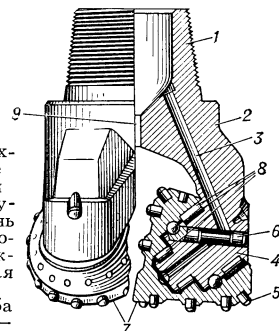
Трёхшарошечное долото для сплошного бурения в очень крепких породах: 1 — наружная конусная присоединительная резьба (ниппель); 2 — секция (лапа) долота; 3 — каналы в лапе и цапфе для продувки опоры; 4 — цапфа лапы; 5 — твёрдосплавные зубки с полусферической рабочей частью; 6 — замковый палец; 7 — шарошки; 8 — подшипники качения; 9 — центральный канал для продувки забоя и шарошек.
